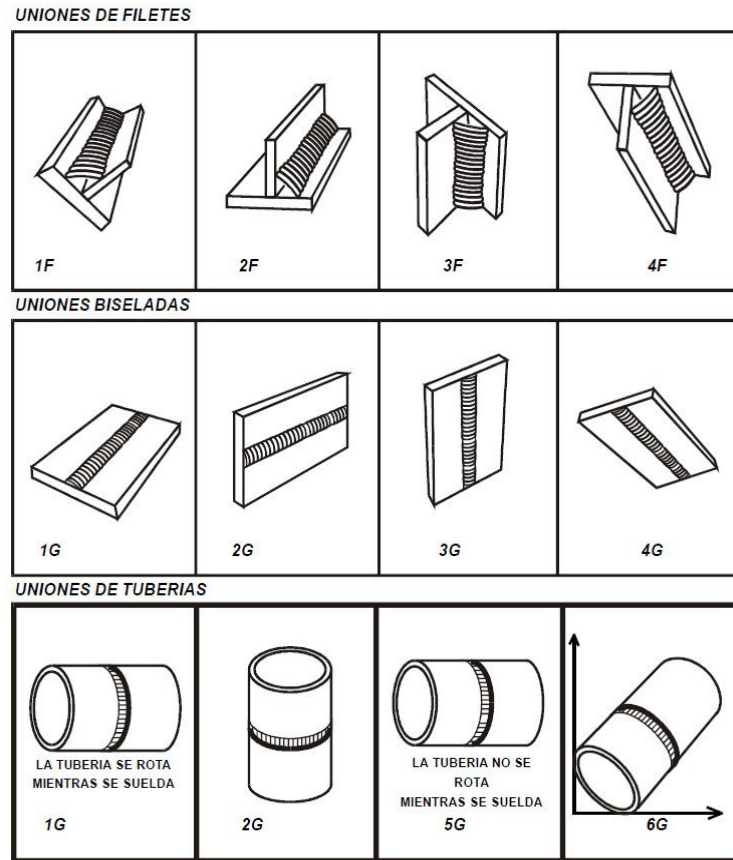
Posiciones de soldadura en Filetes. Tomado de [42, p. 7]
